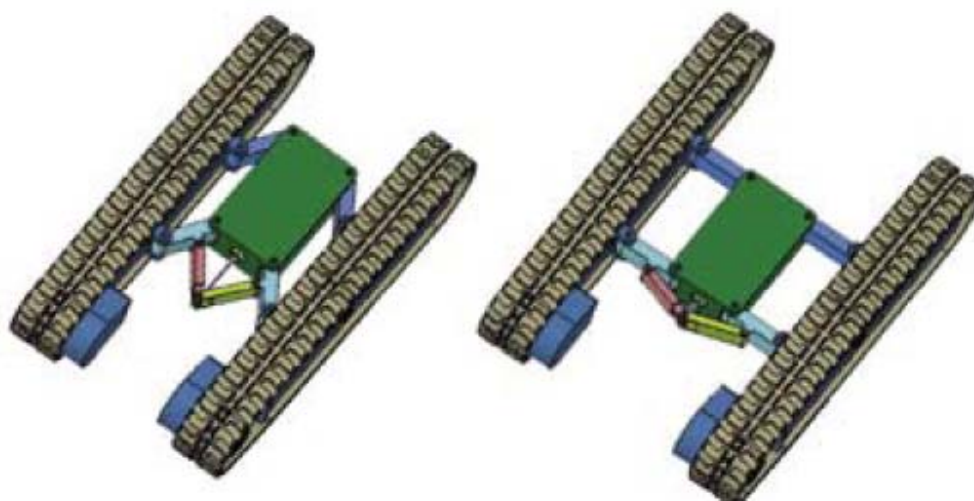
Řešení s posuvnými příčnicí rozdílných průřezů [3]
